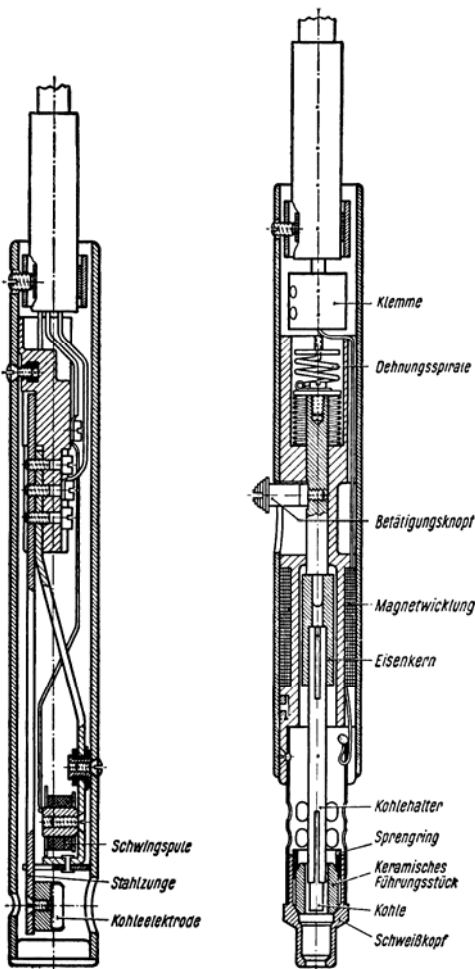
Die beiden Siemens-Schweißwerkzeuge, links die Schwingelektrode, rechts der Schweißgriffel.
